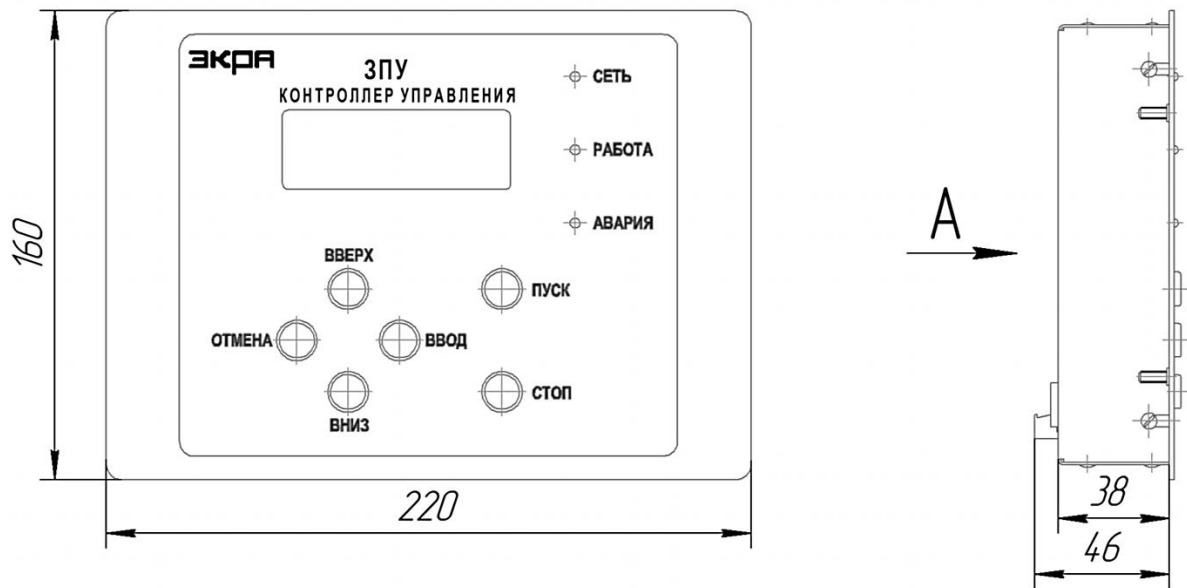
Габаритные и установочные размеры кассеты ЗПУ-10-4
